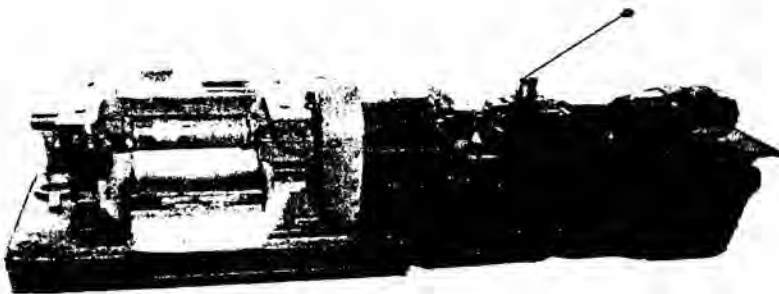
Загальний вигляд стрічкопротяжного стану.
